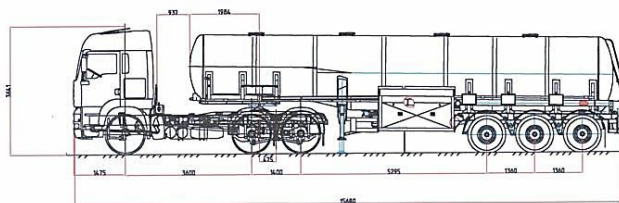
Конструктивна схема газовоза на шасі КамАЗ-6460 типу автопоїзда
